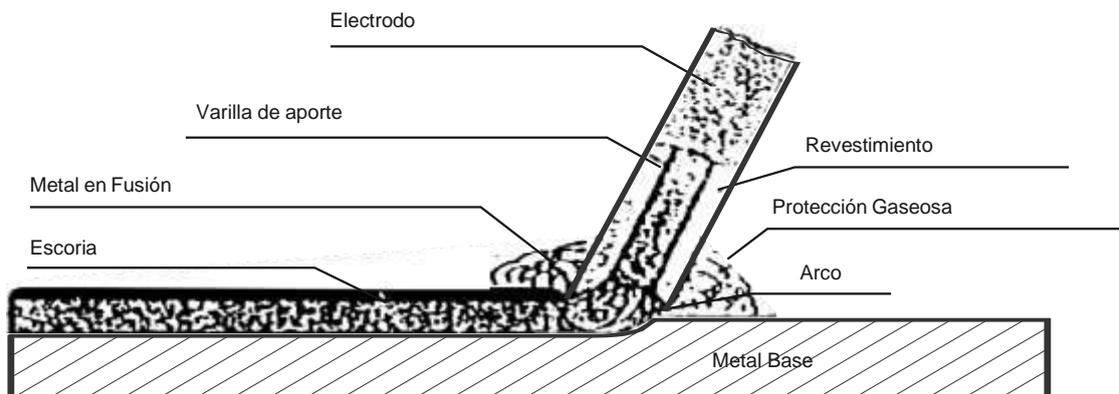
PARTES DEL ARCO ELÉCTRICO
